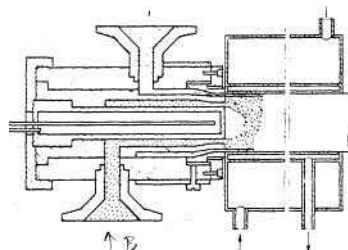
Alat za proizvodnju penastog PVC (Reifenhauser 1961)
